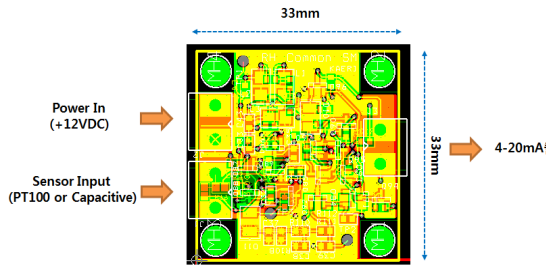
공통센서 신호처리모듈의 PCB 레이아웃
